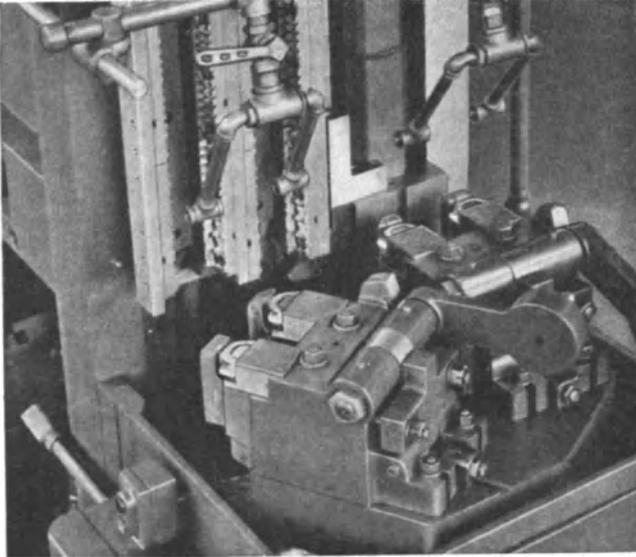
Mehrfachvorrichtung für Zwillingräummaschine.
